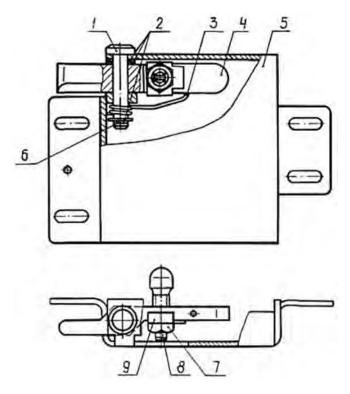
Стопор в сборе: I – ось; 2 – шайба; 3 – пружина; 4 – рычаг; 5 – кожух в сборе; 6 – шплинт; 7 – гайка; 8 – регулятор; 9 – скоба
